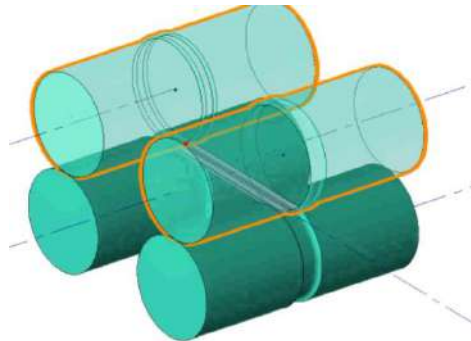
Схема захоплення заготовки у валкову кліть (неусталена стадія процесу)
